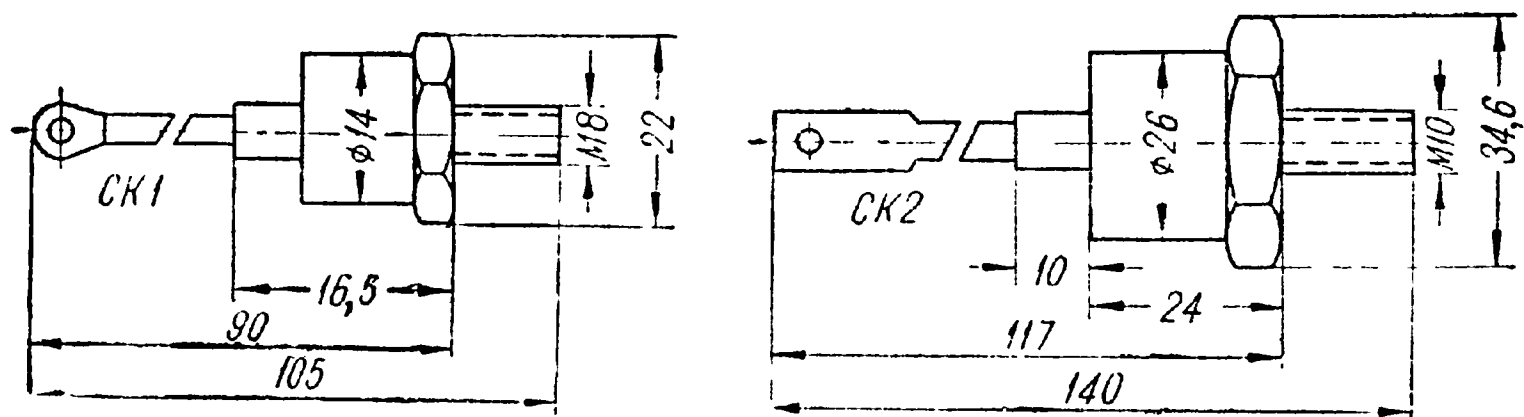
Основные размеры и схематическое изображение стабилизаторов типа СК1 и СК2.
